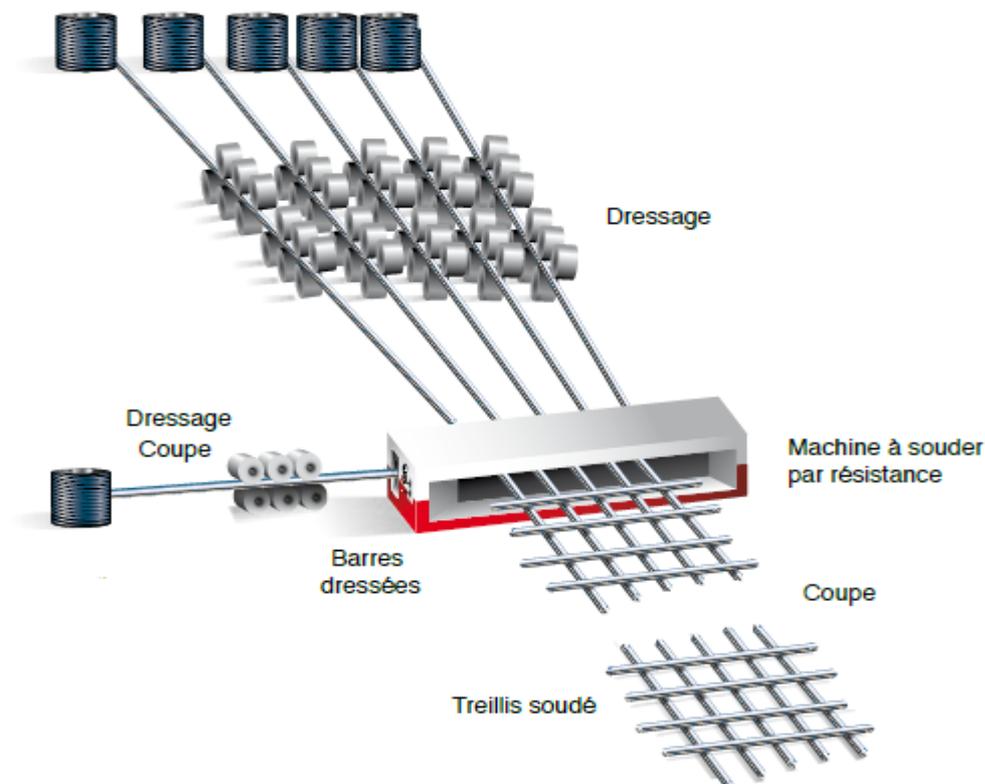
Exemple simple du processus de fabrication du treillis soudé en panneaux
